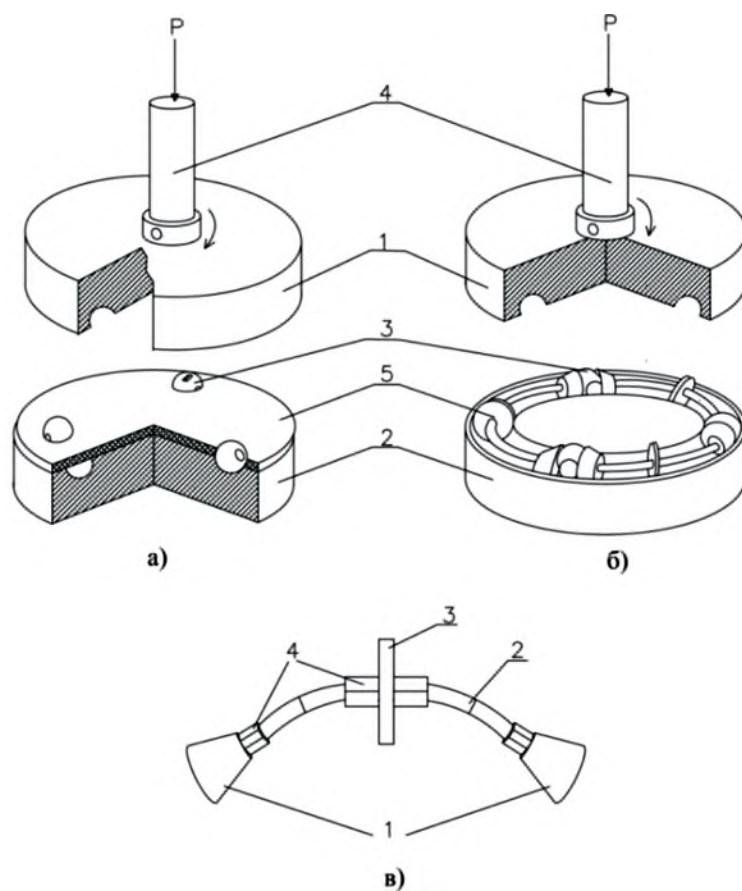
Схема обкатывания пробок между двумя дисками а, б – 1,2 – диски; 3 – сферические детали; 4 – сепаратор; 5 – плавающее крепление; в- 1 – усеченный конус; 2 – дугообразный стержень; 3 – шайба; 4 – гайка
